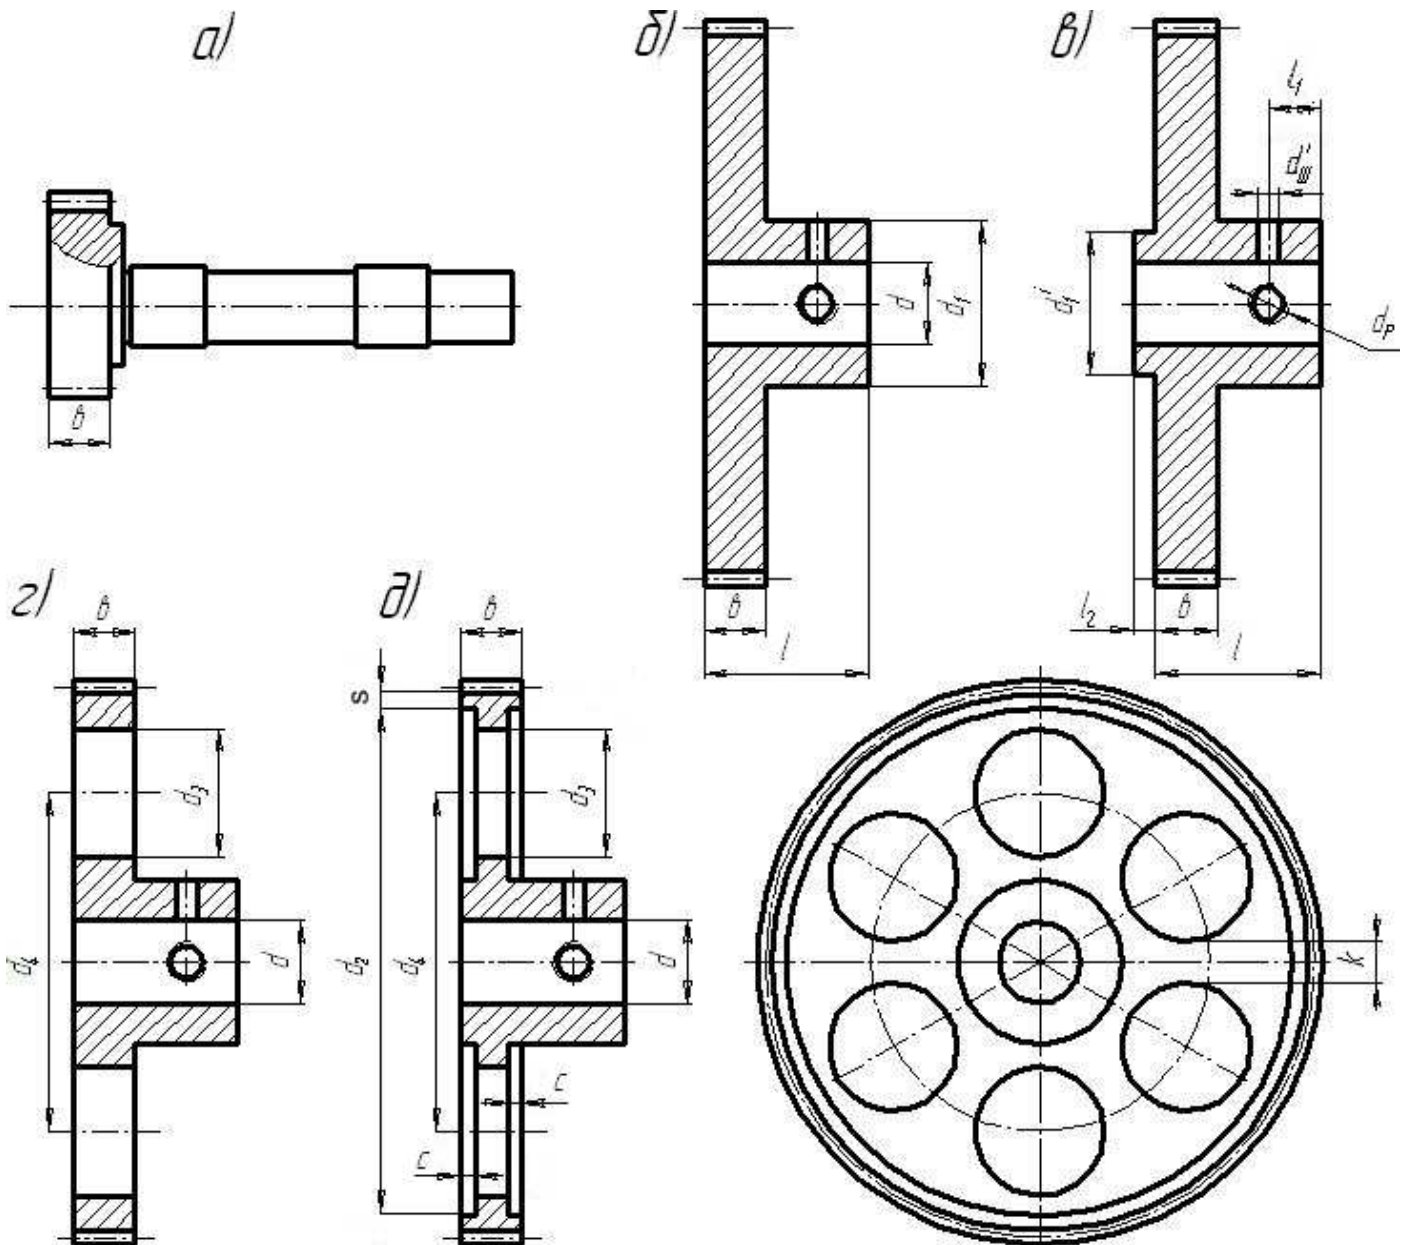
Типовые конструкции цилиндрических зубчатых колёс
